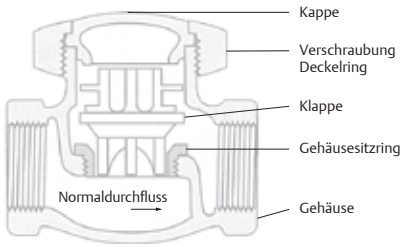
Rückschlagklappe mit horizontalem Hub
